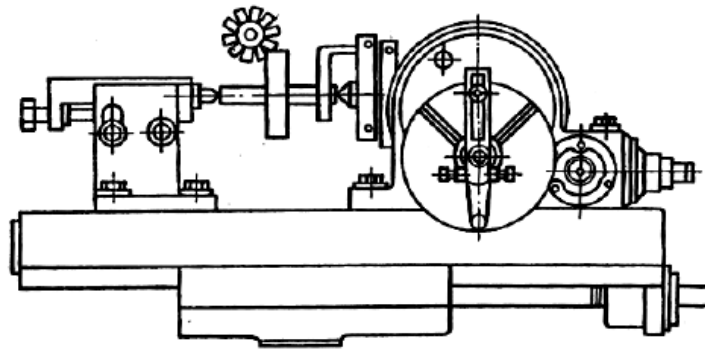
Схема установки для нарізування зубчастих коліс
